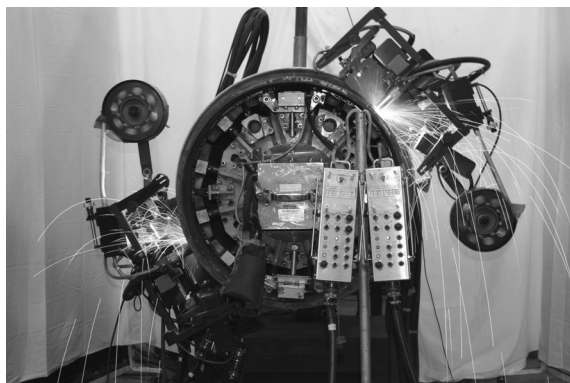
MAG-IIによる2ヘッド溶接状況
